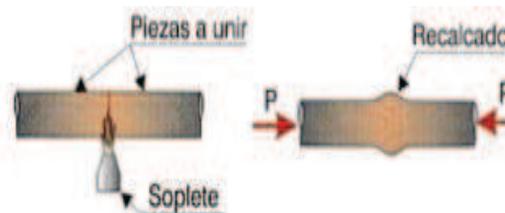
SOLDADURA A TOPE
